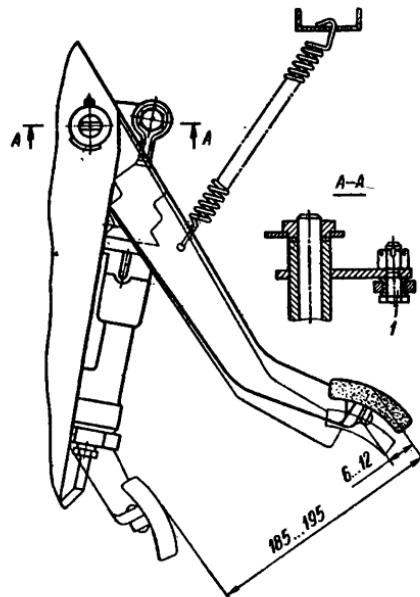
Данные для регулировки и контроля свободного и полного хода педали сцепления:
